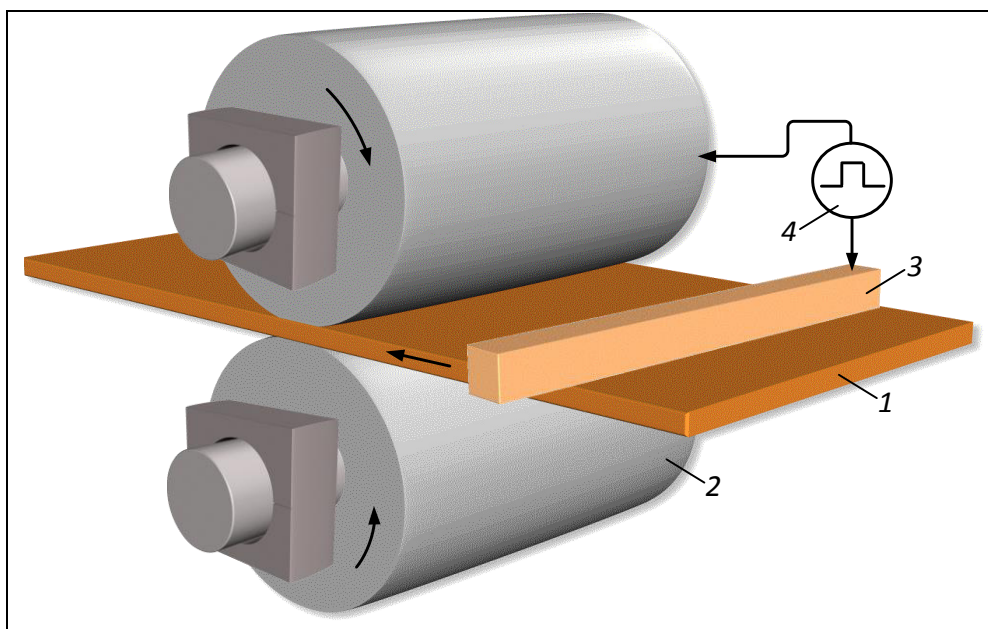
Структура устройства для обработки давлением заготовки 1 из металла с использованием инструментов 2 давления. Дополнительный контакт 3 обеспечивает подключение заготовки к генератору 4 электрических импульсов
